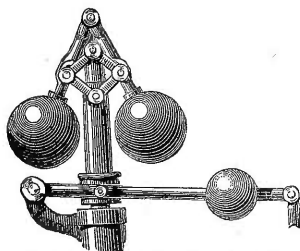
Vue d'ensemble d'un régulateur Andrade.
